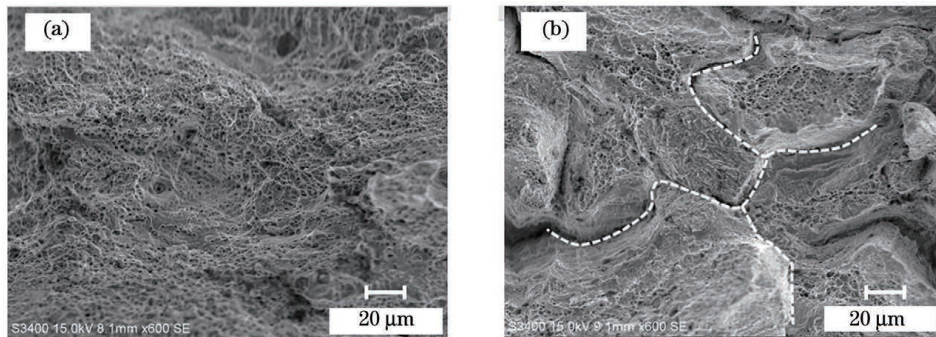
焊接接头的断口形貌。(a)焊接接头上部的断口形貌;(b)焊接接头下部断口形貌
